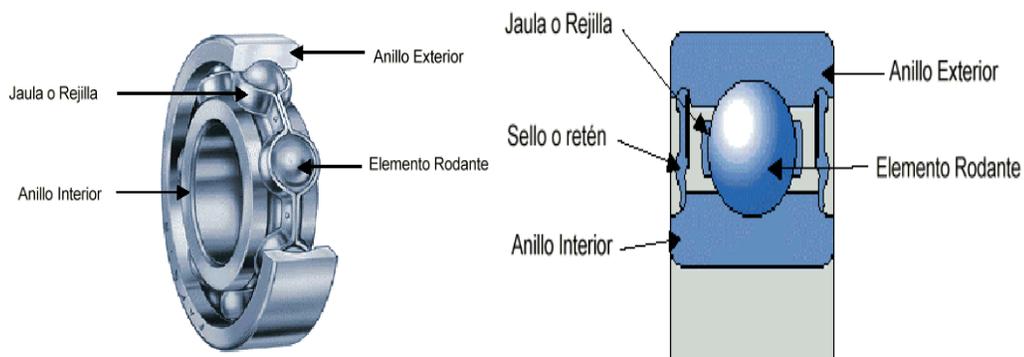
Partes de un rodamiento de bola. [5]
